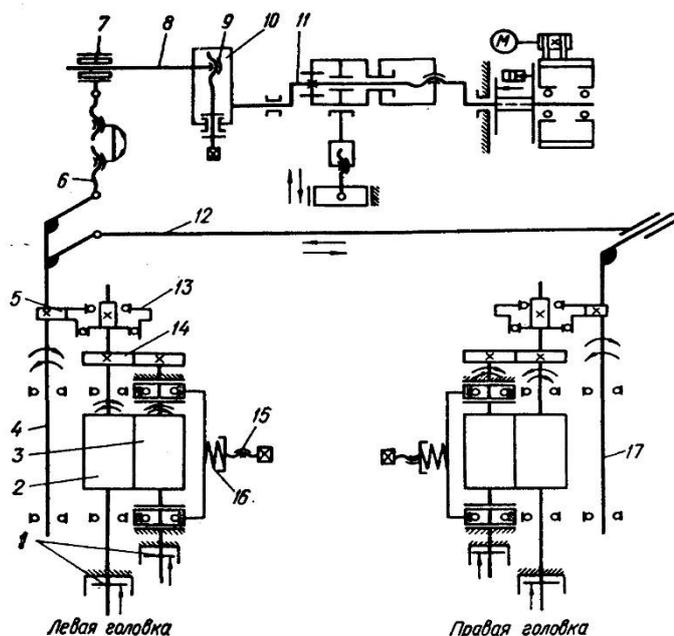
Кинематическая схема двусторонней валковой подачи
